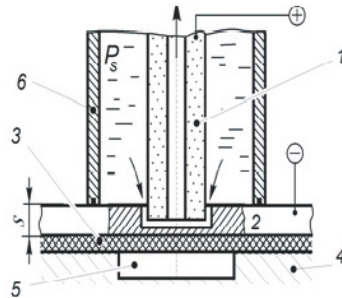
а. - 1-ЕІ; 2-заготовка; 3-гумова підкладка; 4-підкладна плита; 5-камера; 6-гідрокамера
